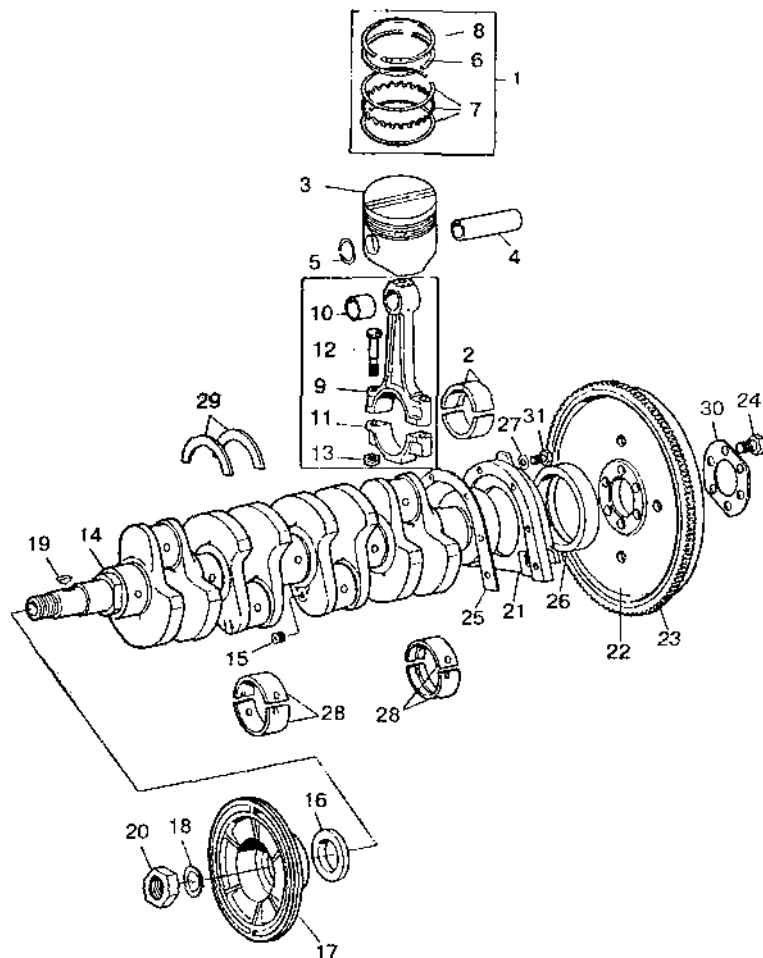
Поршни, шатуны, коленчатый вал:
